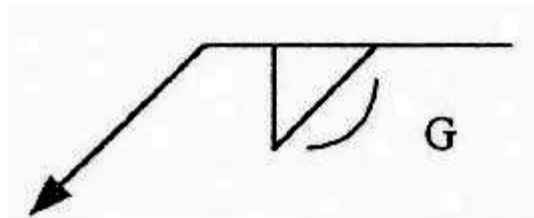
SÍMBOLO DE CONTORNO CONVEXO POR MEDIO DE ESMERILADO EN UNA SOLDADURA DE FILETE
